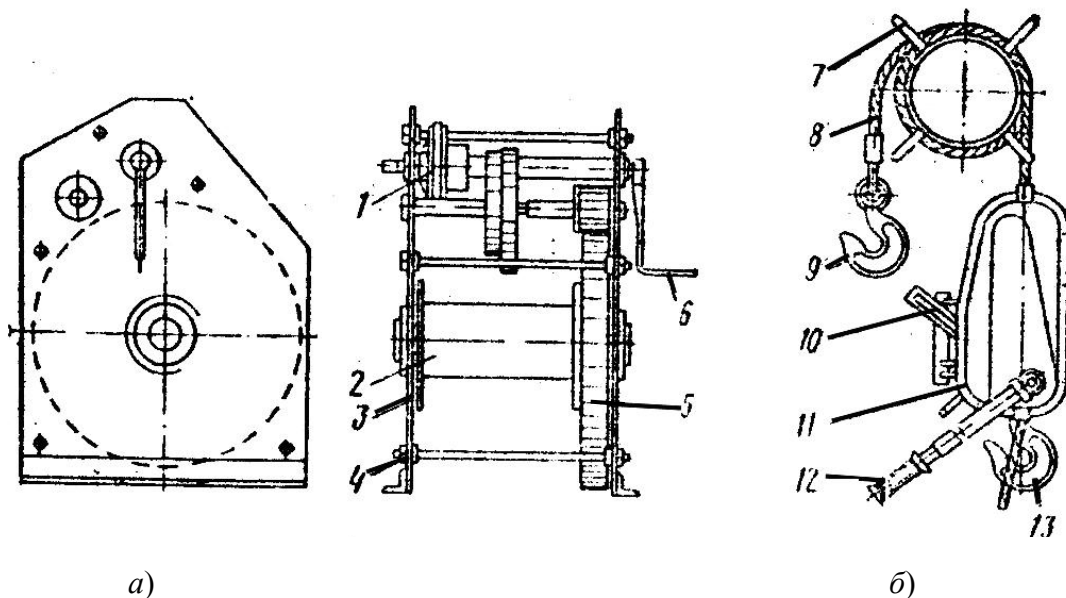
Лебедки с ручным приводом: *а* – шестеренная; *б* – рычажная; 1 – храповое колесо с собачкой; 2 – барабан; 3 – щека; 4 – стяжной болт; 5 – большое зубчатое колесо канатного барабана; 6 – рукоятка; 7 – катушка; 8 – канат; 9 и 13 – крюки; 10 – рукоятка обратного хода; 11 – корпус; 12 – рукоятка переднего хода
